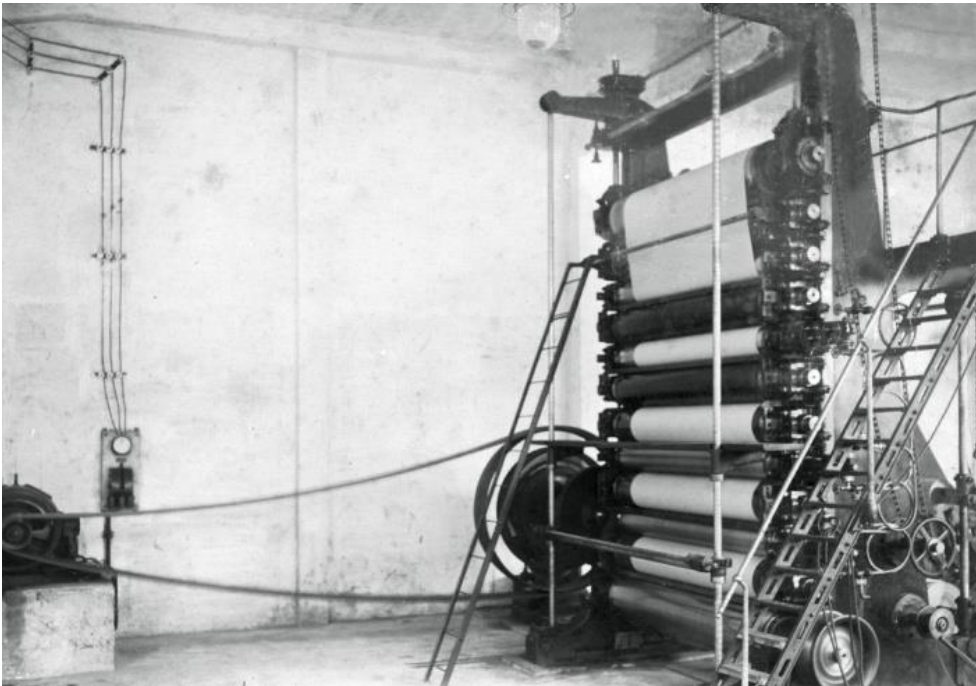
Calandra de la papelería Portu de Zizurkil. (AMV)
